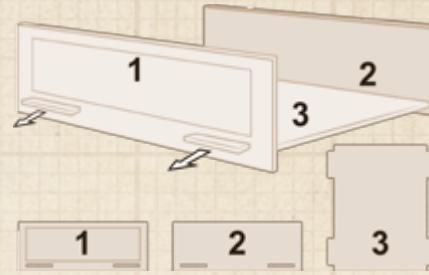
«Tiroir de défausses» et instructions d'assemblage.
